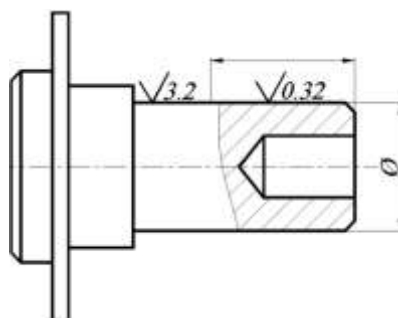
Обозначение участка с различной шероховатостью одной поверхности
